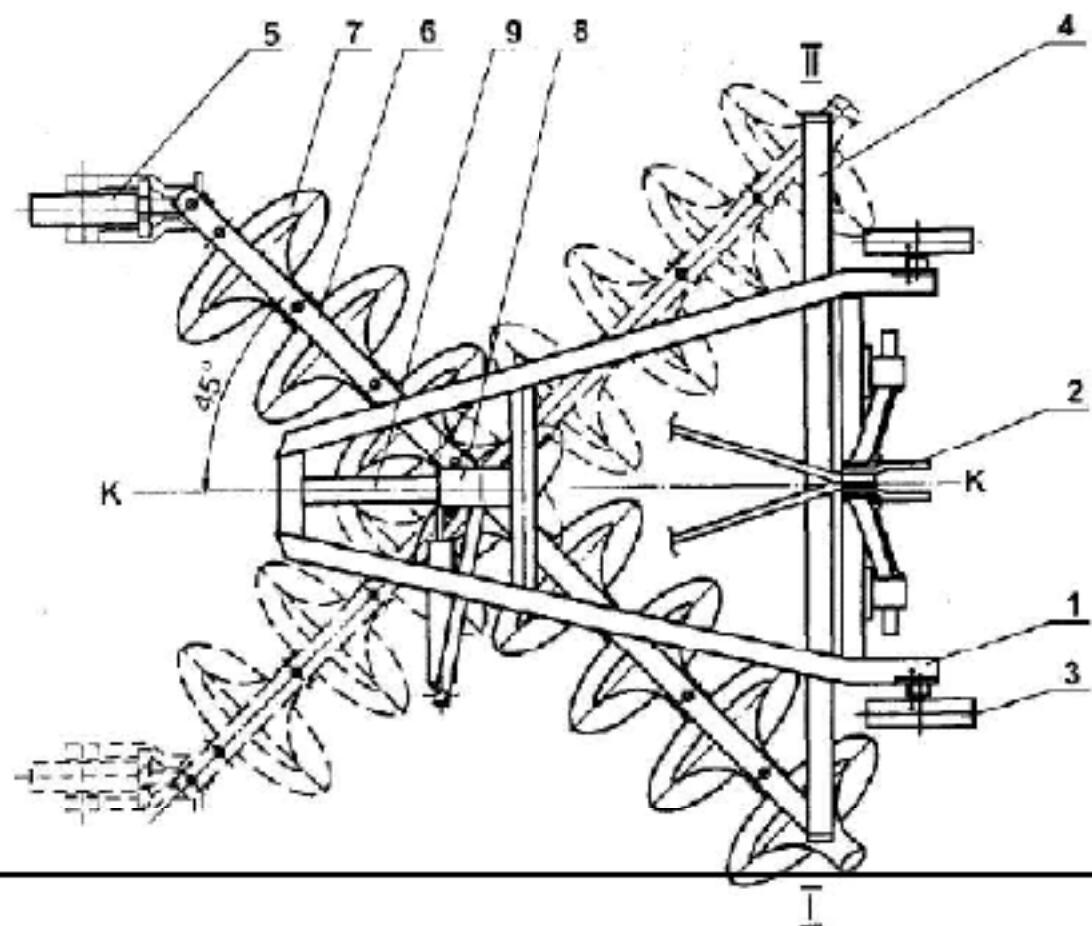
Конструктивная схема поворотного дискового плуга
